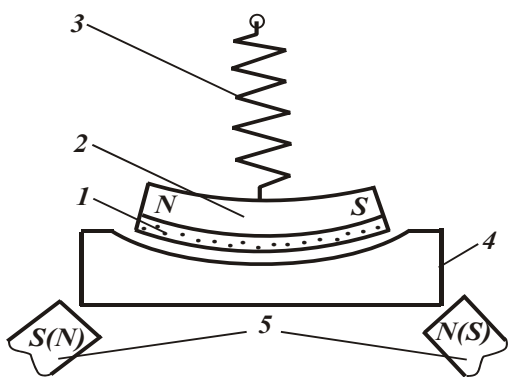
Маятниковая схема электроискрового магнито-импульсного шлифования вогнутых сферических поверхностей: 1 – шлифовальный инструмент; 2 – патрон для шлифовального инструмента из намагниченного материала или с электромагнитом; 3 – пружина подвески патрона со шлифовальным инструментом; 4 – обрабатываемая деталь; 5 – электромагниты.
